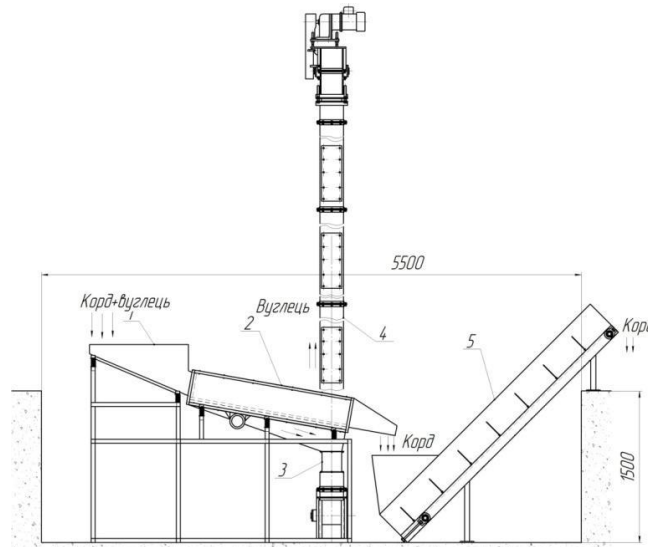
Технологічна схема для механічної очистки технічного вуглецю
